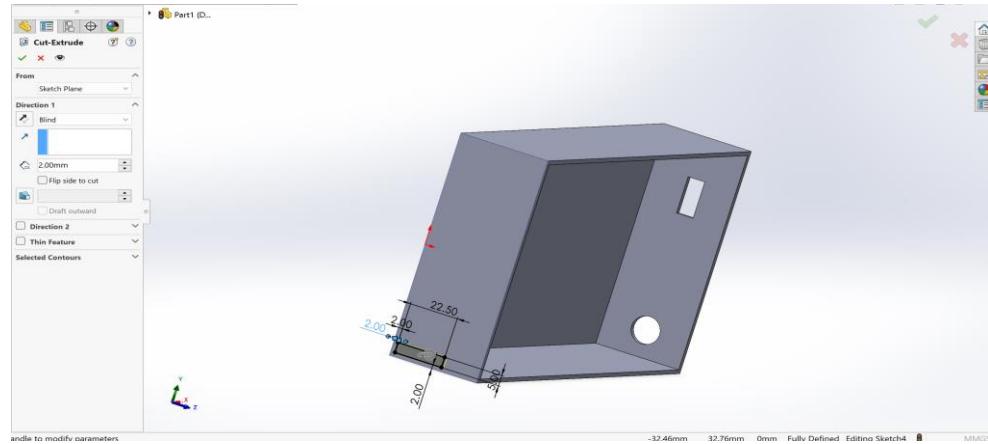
7 Fitur Extrude Bose/Base Pada Casing PCB
